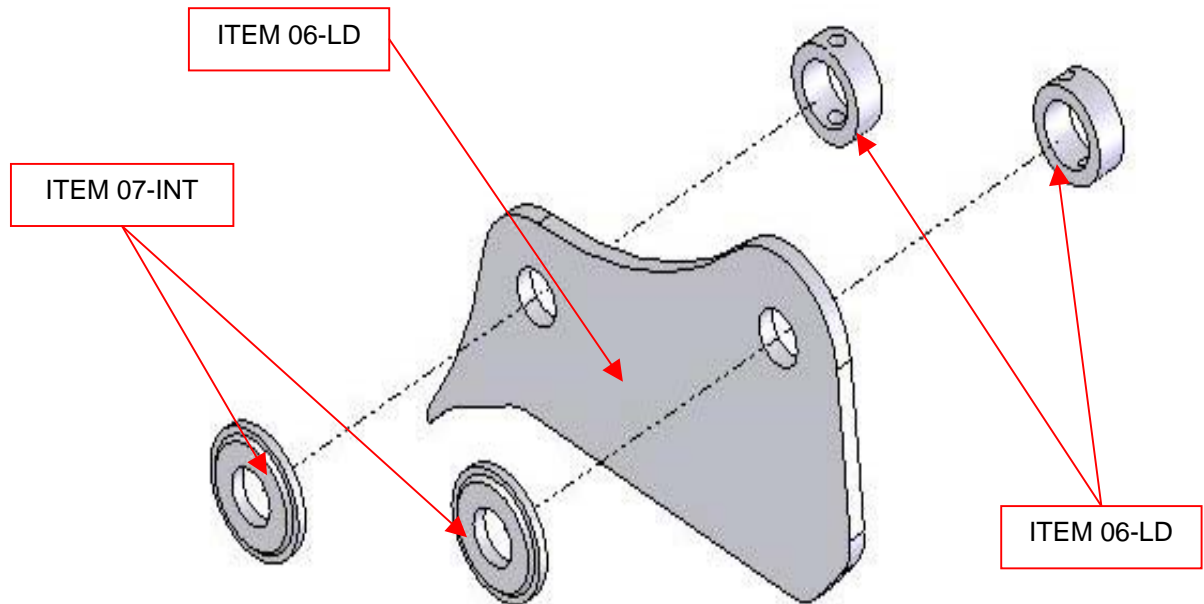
Vista explodida do subconjunto 03 - SC03.
